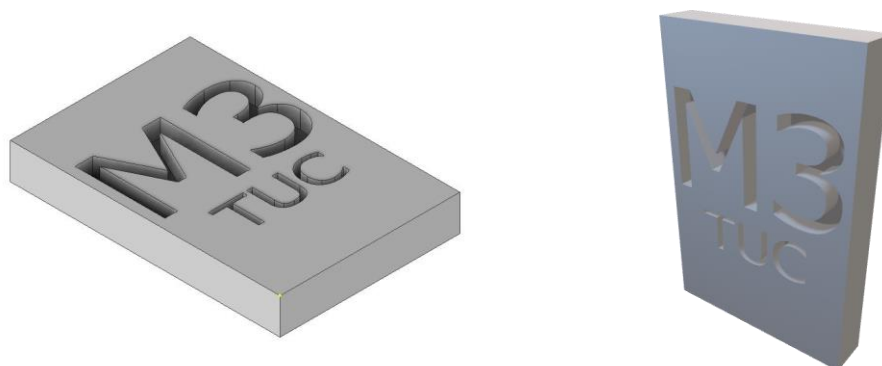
Τρισδιάστατη απεικόνιση αποστολής 35
